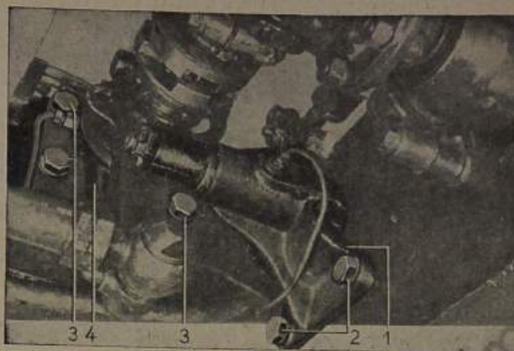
Linken Lagerbock für Lenkzwischenwelle abschrauben
